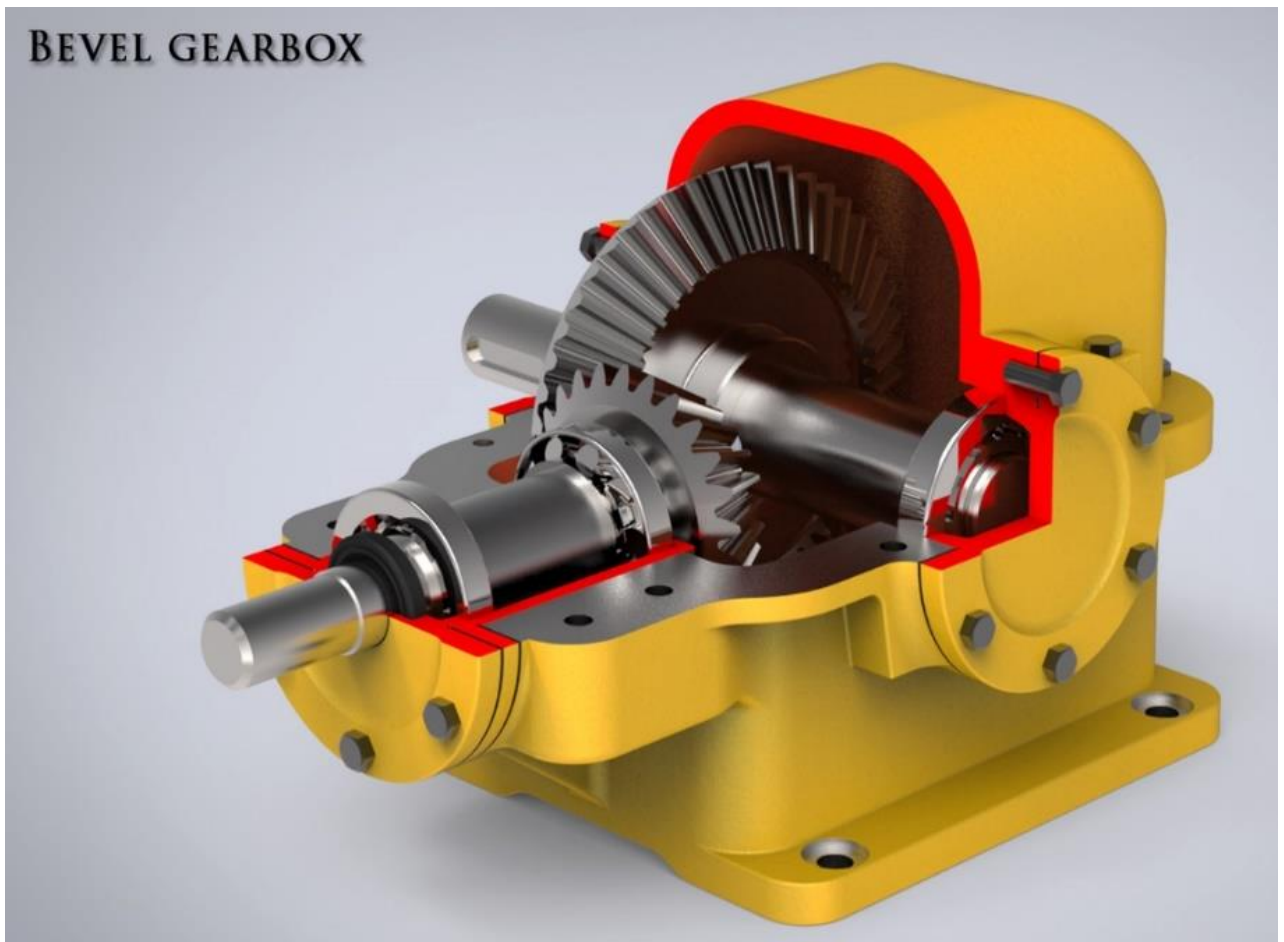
Редуктор одноступінчастий конічний, загальний вигляд [59]
